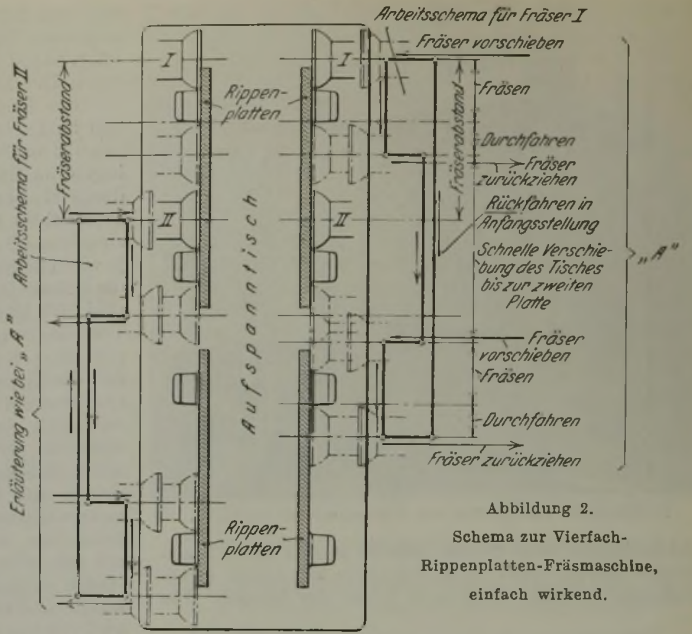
Schema zur Vierfach-Rippenplatten-Fräsmaschine, einfach wirkend.
